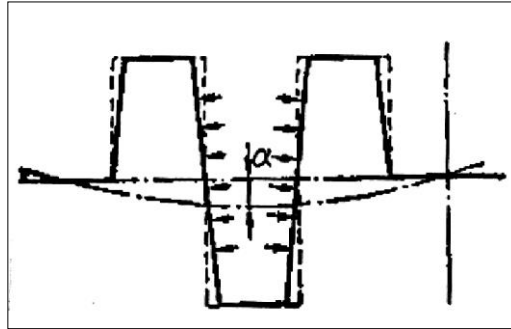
Правка колінчастого вала місцевим наклепом
